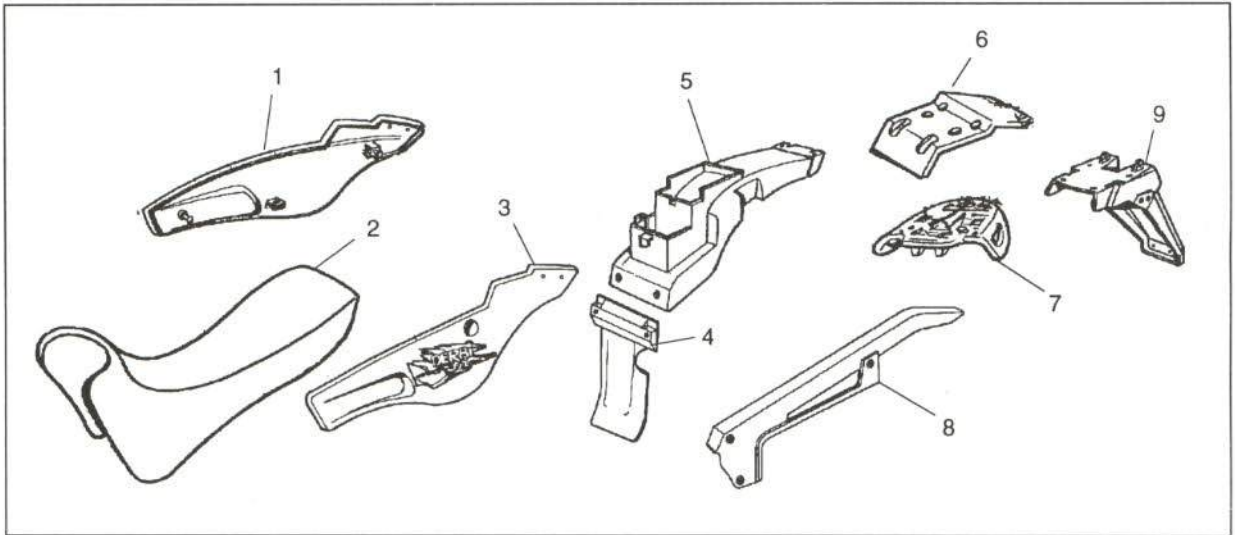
Despiece de las piezas exteriores de la parte trasera.
